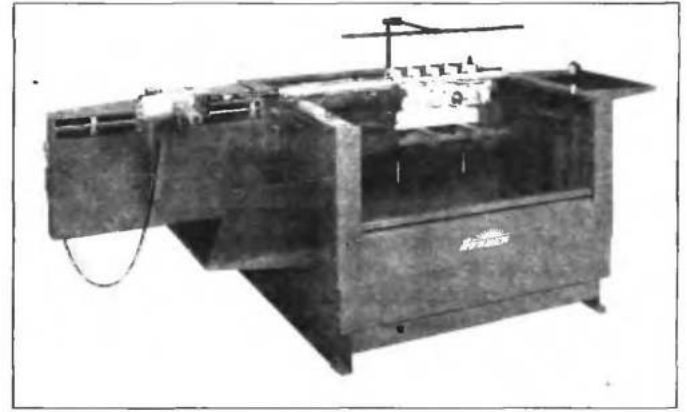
Горизонтально-хонинговальный станок для постелей подшипников
